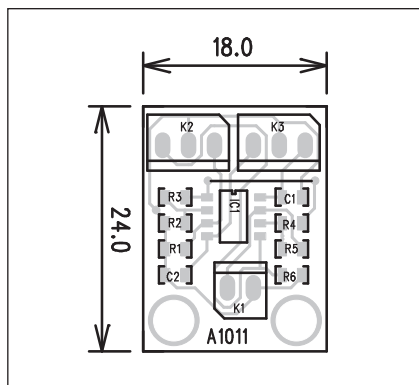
Obrazec desky spojů výstupního zesilovače (strana BOTTOM)
